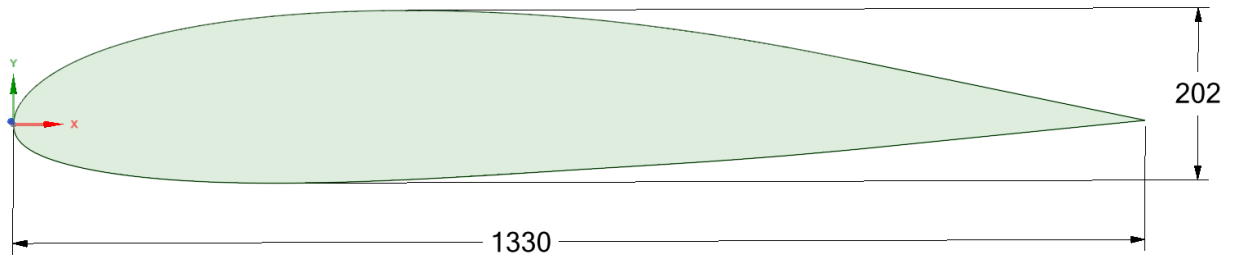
Dimensiones principales del perfil GA30315, mm
